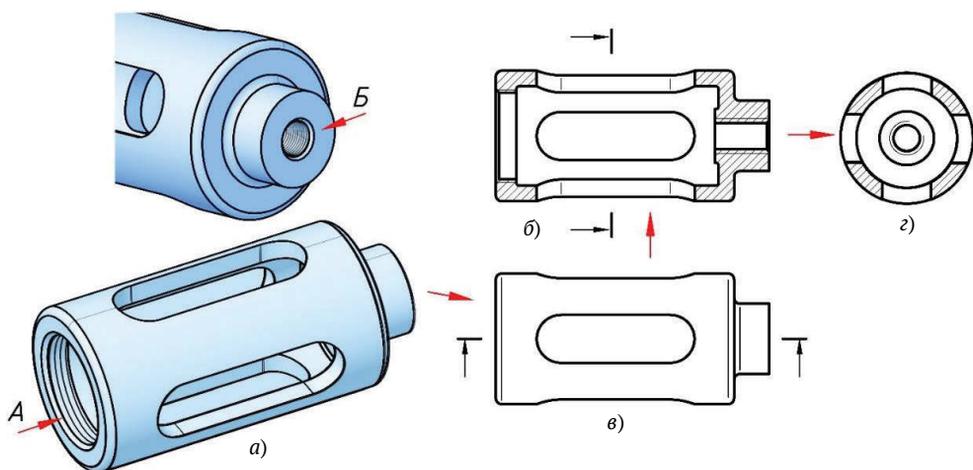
Корректировка модели и схема построения рабочего чертежа детали «корпус»: а – нанесение 3D-резьбы и 3D-фаски; б – 2D-вид сверху; в – фронтальный 2D-разрез; г – профильный 2D-разрез
